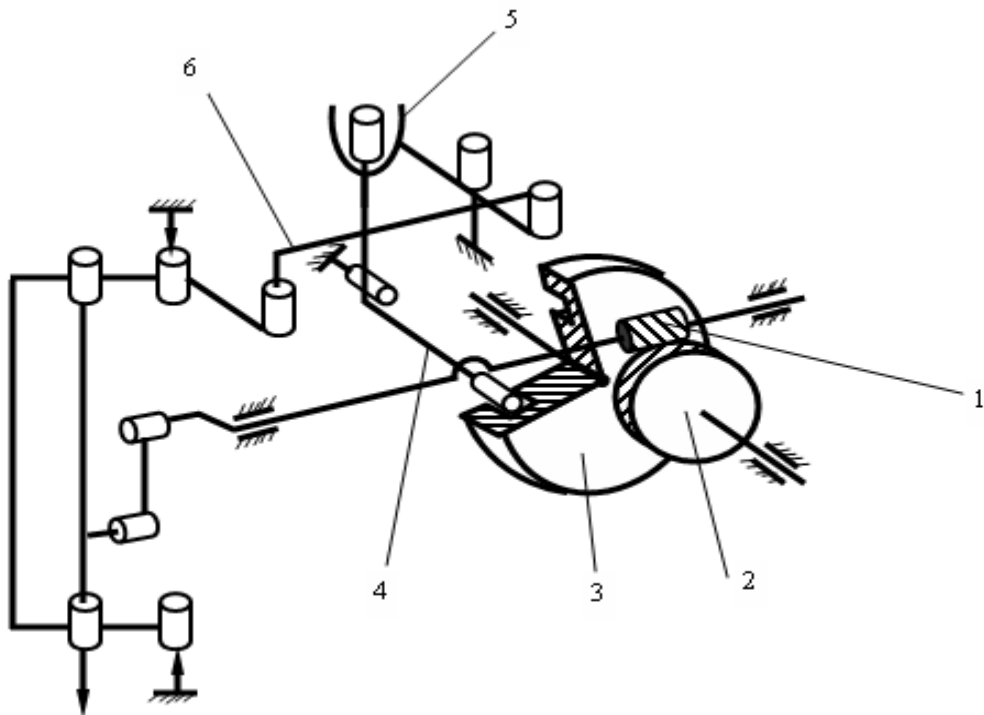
д – Схема кинематики иглы механизма полуавтоматической швейной машины класса 27: 1 - червяк; 2-червячное колесо; 3-копирный диск; 4 – вертикально расположенный рычаг; 5 - горизонтальная кулиса; 6-тяга
